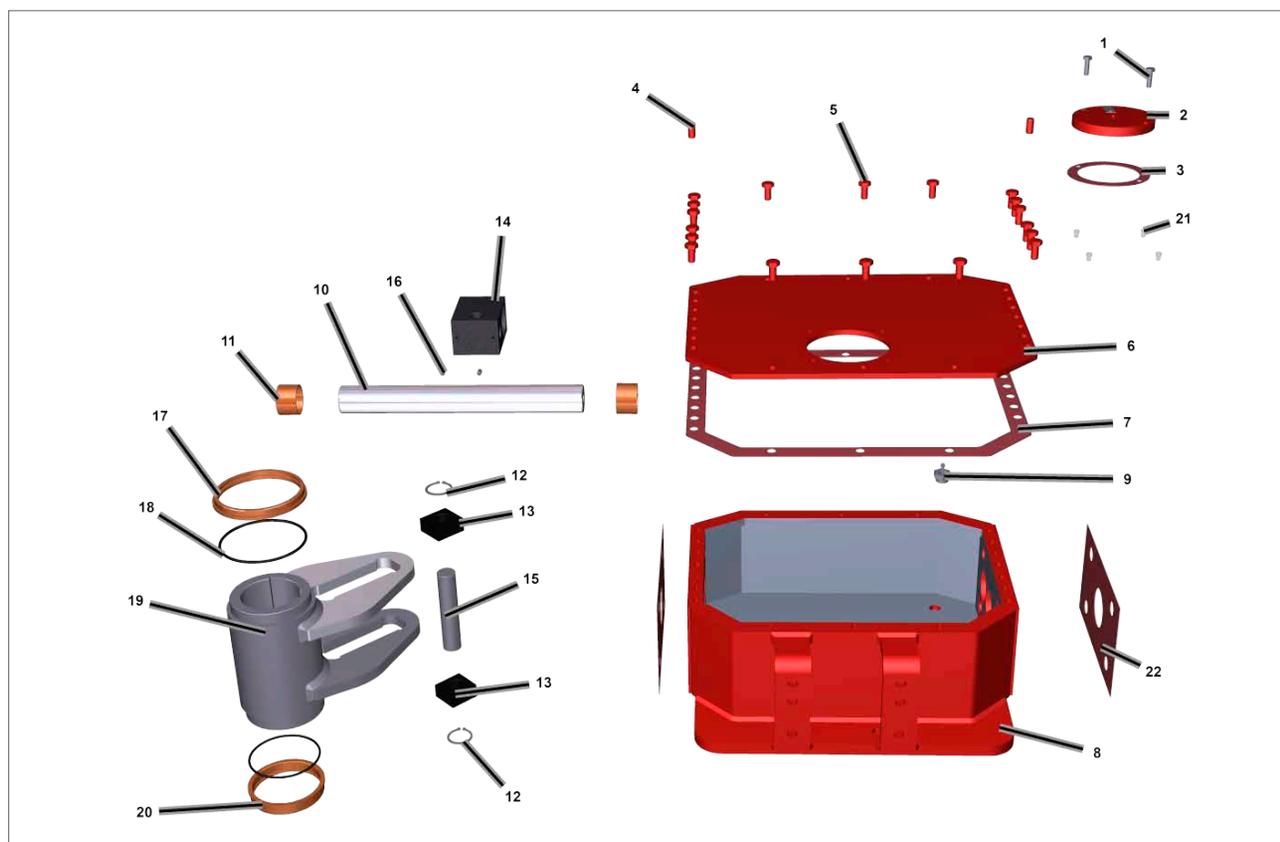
Carter principal (soudé) (taille de l'actionneur 065, 85, 100, 130, 161, 350)
